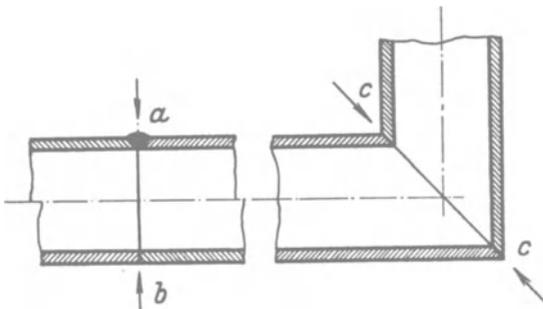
Nahtschweißungen an Gasrohren.
